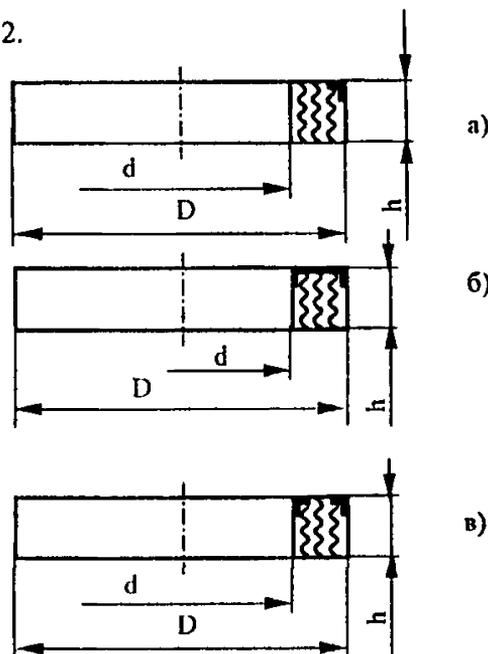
Конструкция кольца из ТРГ для узла бесфланцевого соединения корпуса и крышки арматуры:
